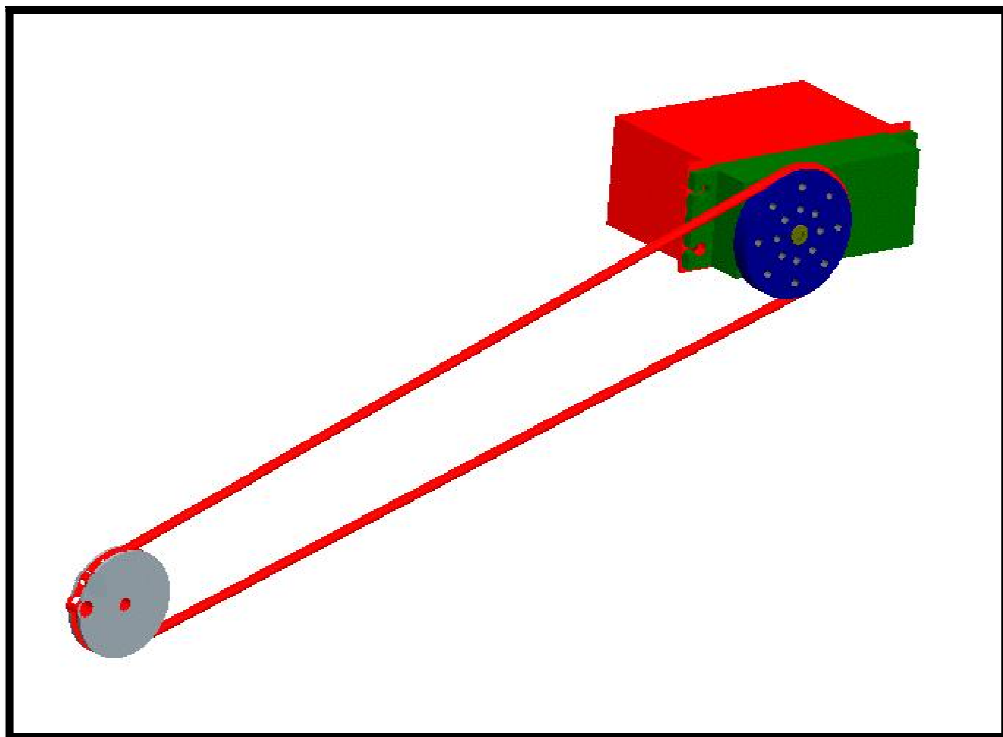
Diseño tridimensional del mecanismo propuesto
